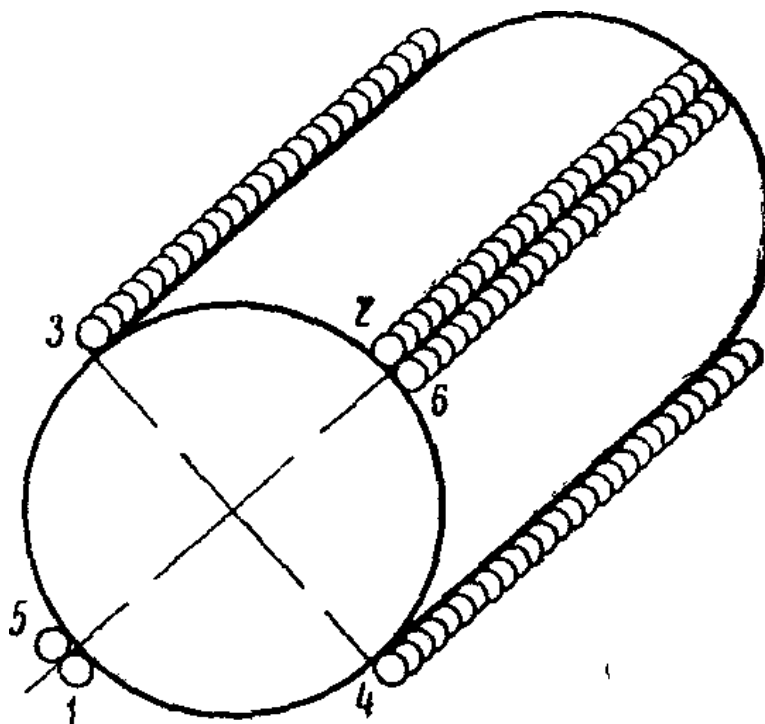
Наплавка изношенной шейки вала продольным наложением швов, последовательность наплавки: 1—2—3—4—5—6 и т.д.
